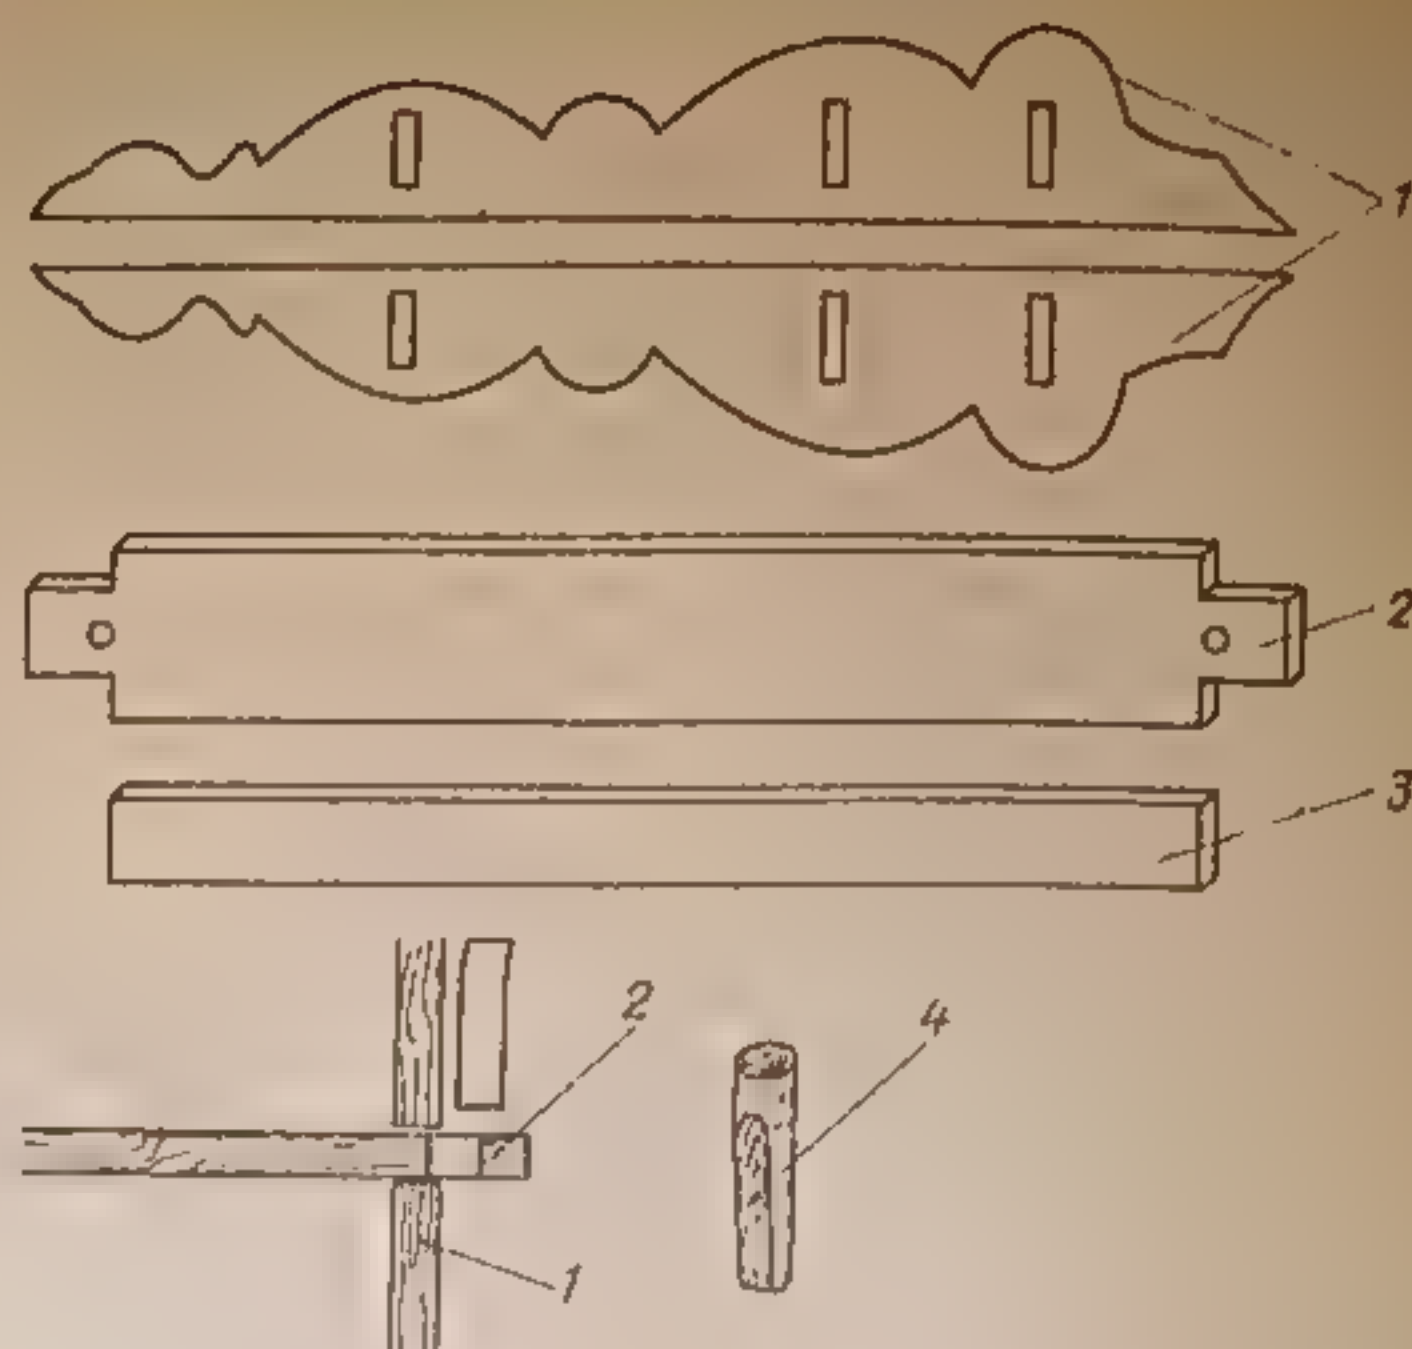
Детали полки: 1 — боковины; 2 — верхняя полка; 3 — вертикально расположенная доска; 4 — клин
